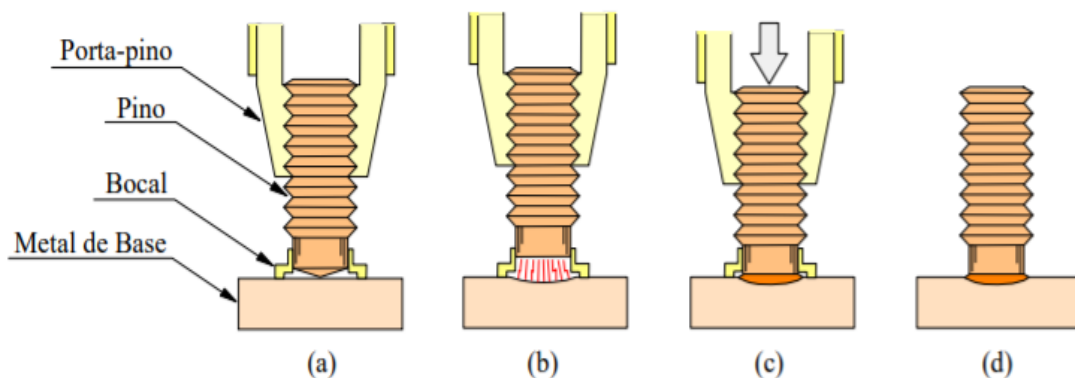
Sequência de soldagem de pinos em um processo Stud Welding (SW). Da esquerda para a direita o processo ocorre desde o contato do pino com a peça até a deposição completa do material.
